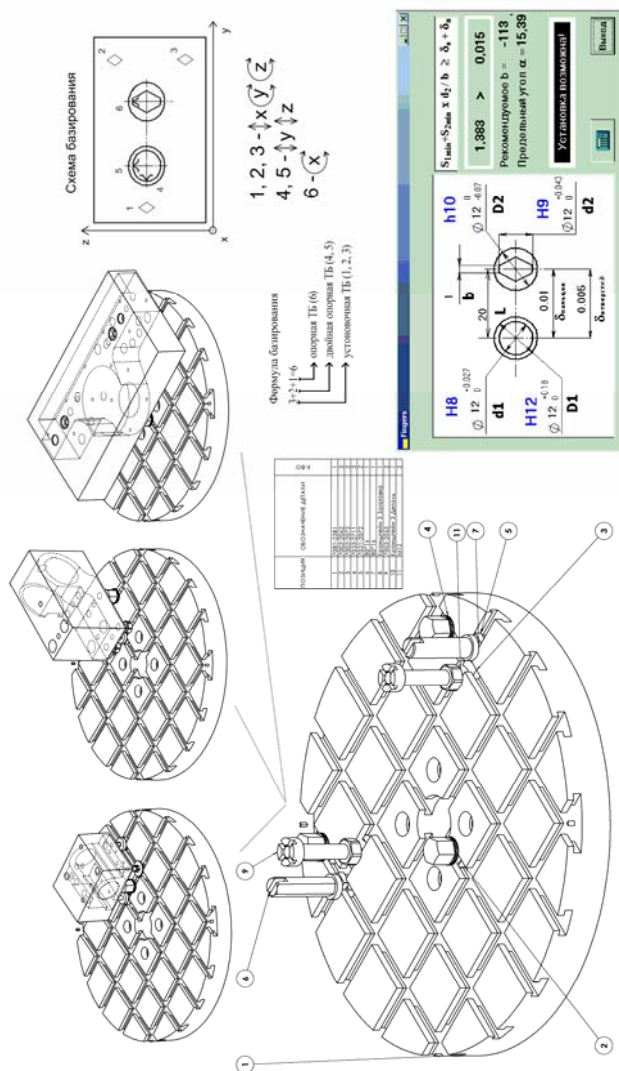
Структура и параметры группового зажимного приспособления для обработки деталей типа „Кронштейн” и др.).
